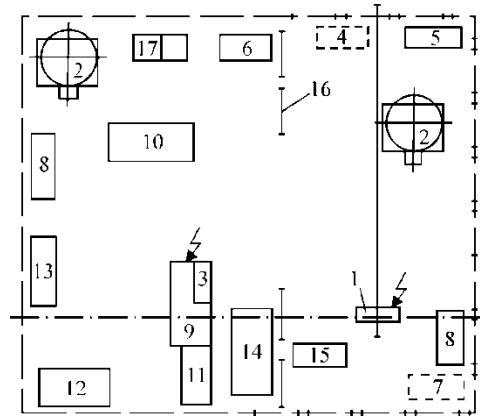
Робоче місце слюсаря з ремонту кабін (площа 48 м²): 1 – кран-балка підвісна; 2 – стелаж для деталей; 3 – стенд поворотний для ремонту кабін; 4 – ящик для обтирального матеріалу; 5 – плита перевірна; 6 – установка для газополуменевого розпилення порошку легкоплавких матеріалів; 7 – щит для зварювальних робіт; 8 – річний шліфувальний верстат з гнучким валом; 9 – шланговий напівавтомат для зварювання в середовищі вуглекислого газу; 10 – шафа для інвентарю; 11 – візок для кисневих балонів; 12 – стіл для газозварювальних робіт; 13 – стелаж для зберігання скла; 14 – стіл монтажний металічний; 15 – верстак слюсарний; 16 – настільно-свердлильний верстат; 17 – шафа для монтажних пристосувань
